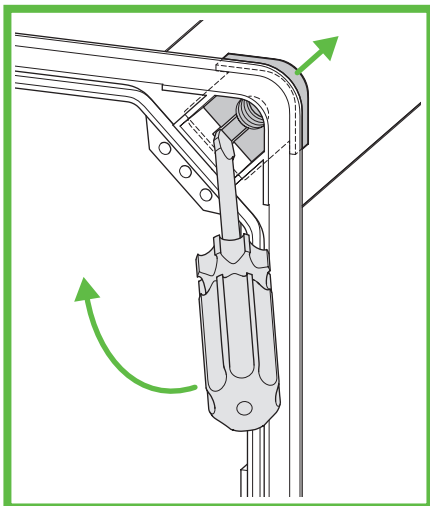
Demontage Gewindeeinschübe GEOS 3030, GEOS 3040 GEOS 4050
